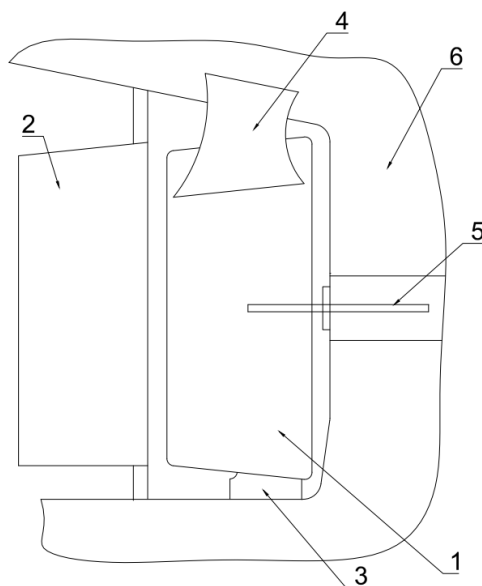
Загальний вигляд та встановлення насадки на траулері: насадка траулера з її установкою: 1 – Насадка; 2 – Перо керма; 3 – Нижня бракета; 4- Верхня бракета (2шт); 5 – Горизонтальна бракета (2 шт); 6 – Корпус судна.
